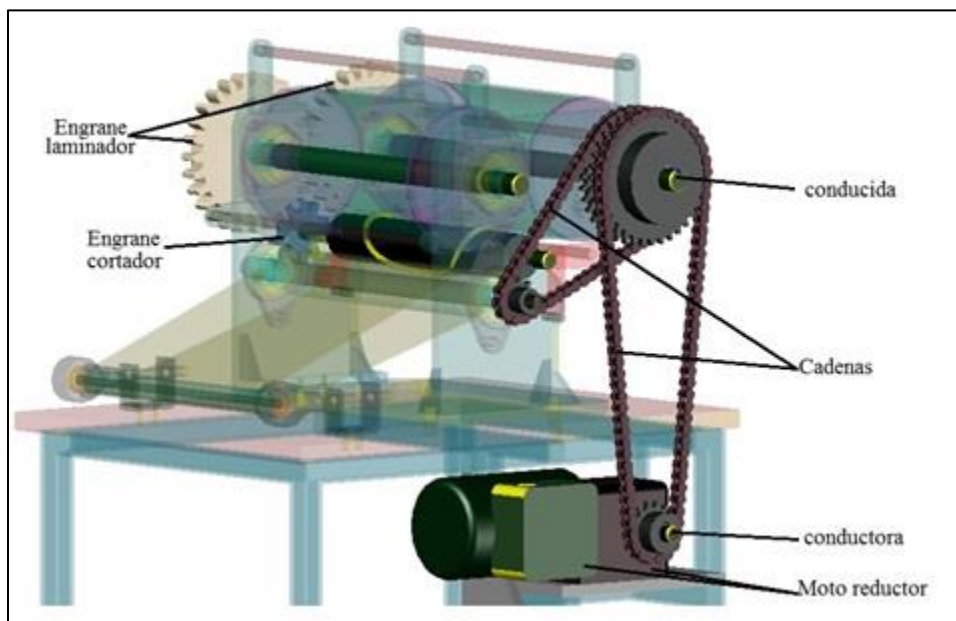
Transmisión rodillo-laminador (Fuente propia).
